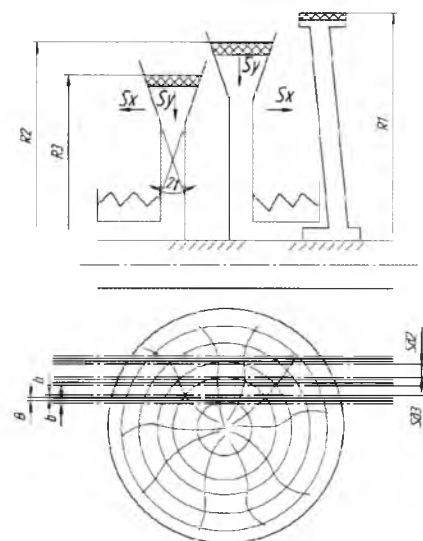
Схема для расчёта значений передаточного числа пильных шкивов вариаторного типа
